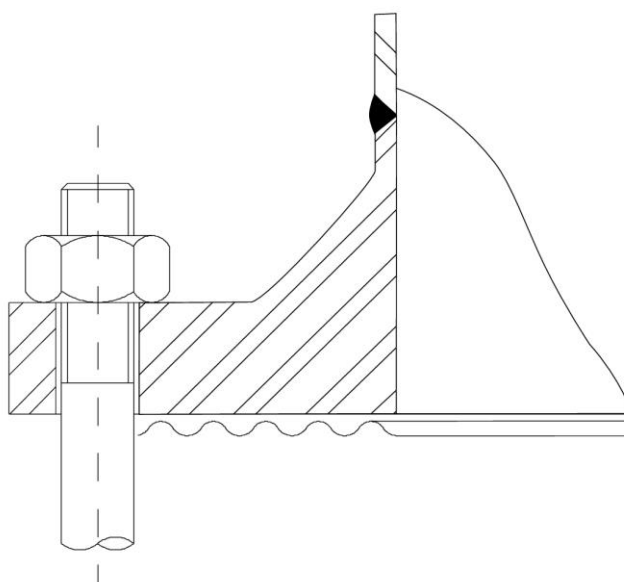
Junta metálica corrugada. (VEIGA, 2014)
